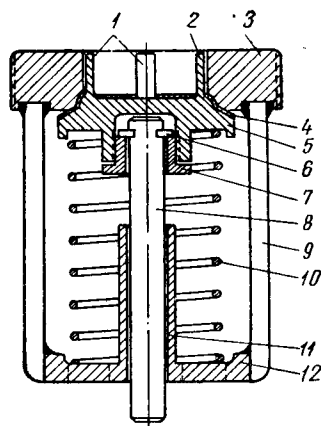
Обратный клапан конструкции Титкова и Дона.
